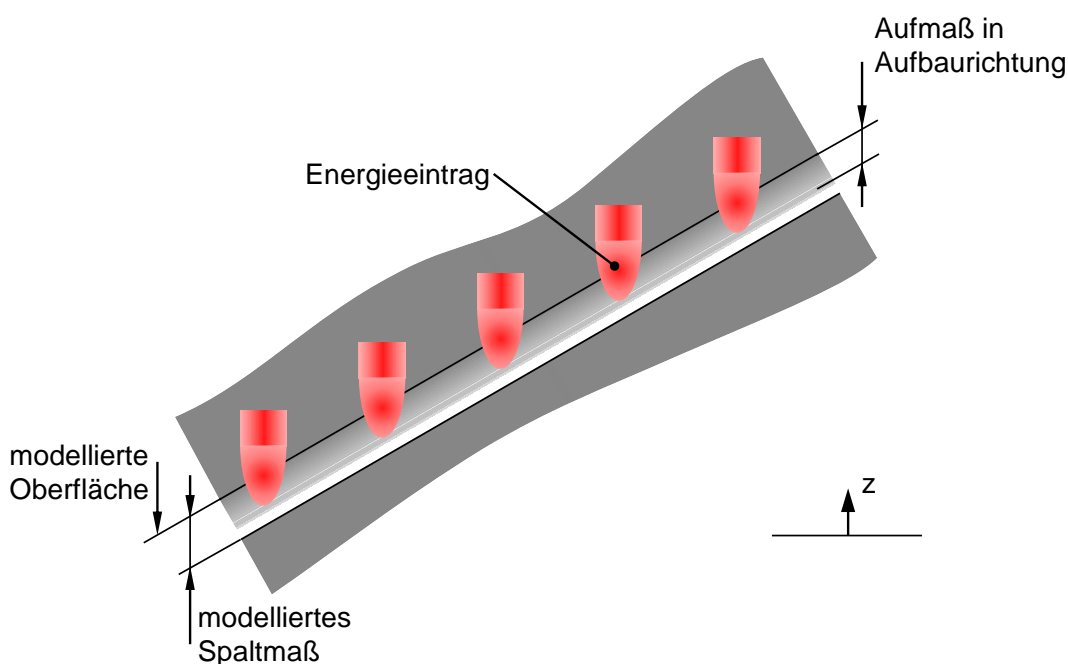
Minimales Spaltmaß in Aufbaurichtung
